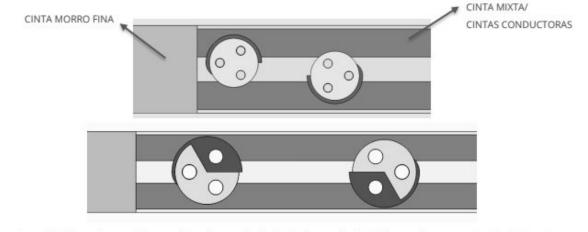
Colocación arandelas metálicas de conexión (gris claro) pequeñas (arriba) y grandes recortadas (abajo). En gris oscuro bajo la arandela metálica de conexión se encuentra la arandela plástica.
